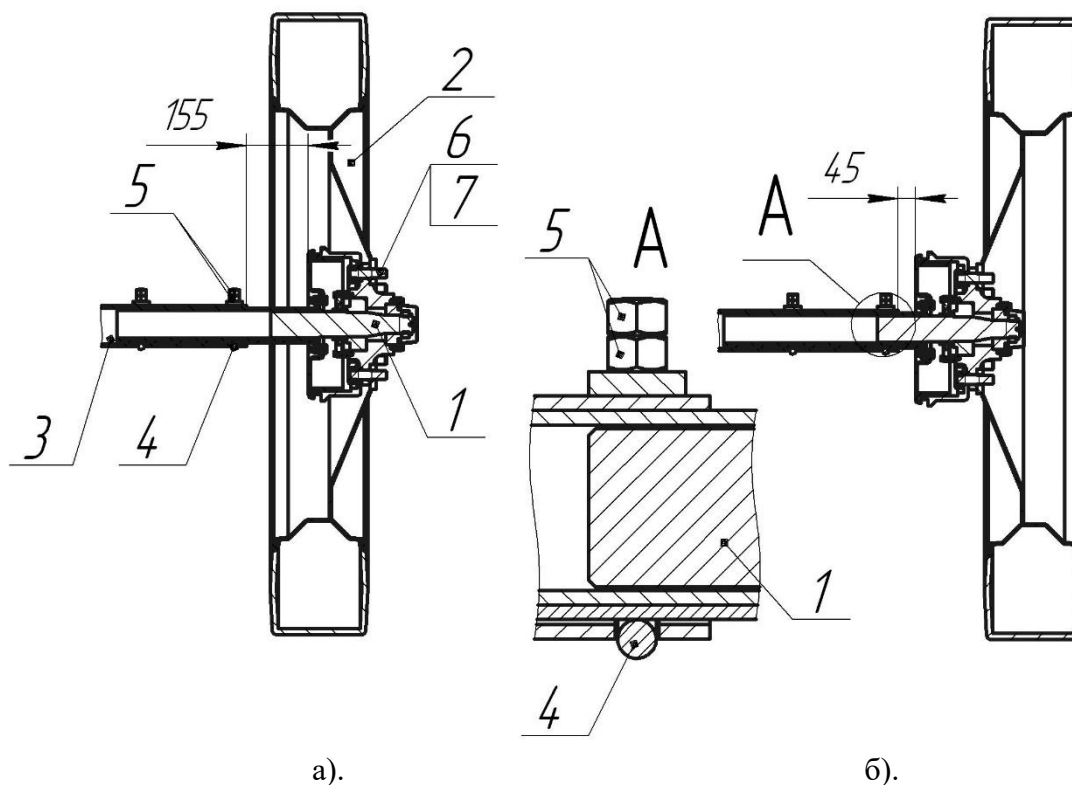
Схема установки колес при колее, а) 1500 мм, б) 1800 мм.
